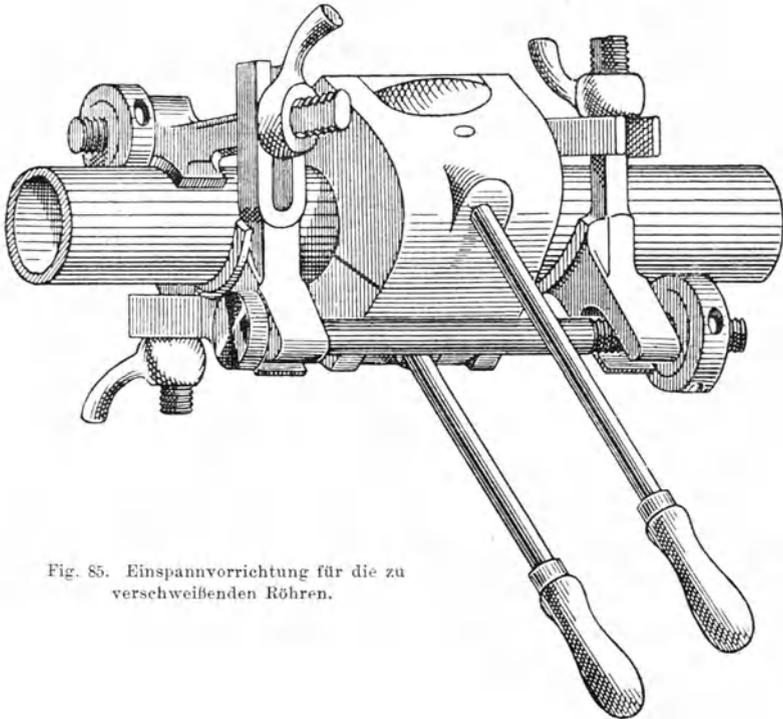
Einspannvorrichtung für die zu verschweißenden Röhren.
